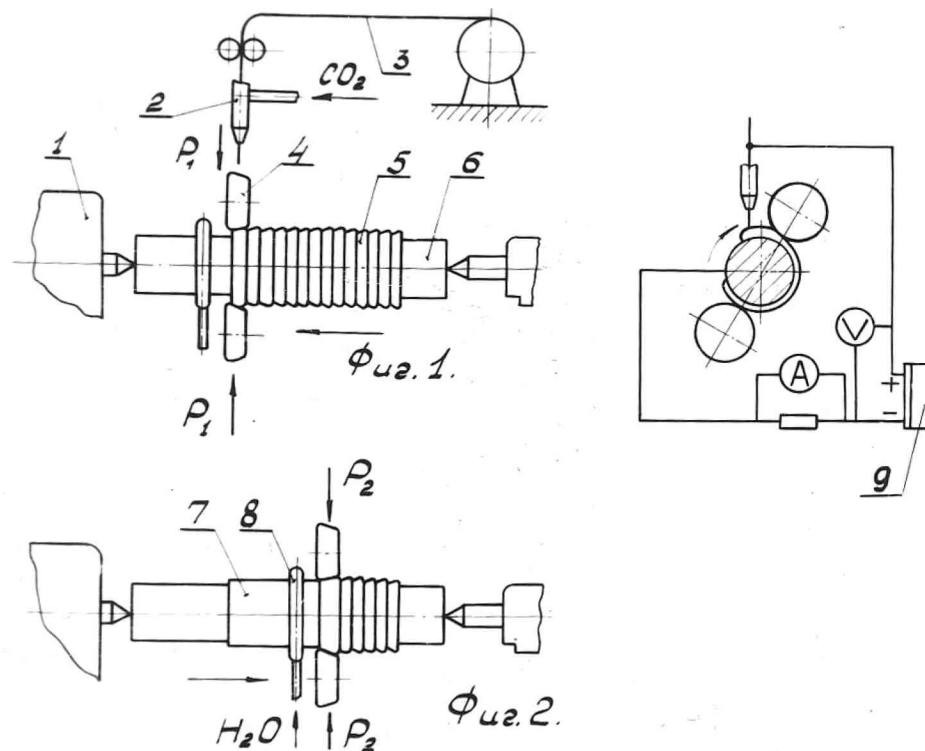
Схема проведення ВТМО в процесі наплавлення і НТМО після її припинення. а - ВТМО; б - НТМО 1 - верстат; г - наплавочна головка; 3 - зварювальний дріт; 4 - деформуючі ролики; 5 - наплавлений метал після ВТМО; 6 - деталь; 7 - наплавлений метал після НТМО; 8 - спреєр; 9 - випрямляч
